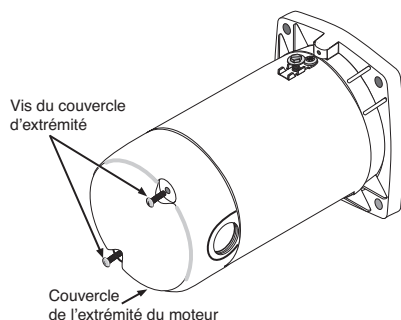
Retrait du couvercle de l'extrémité du moteur.
